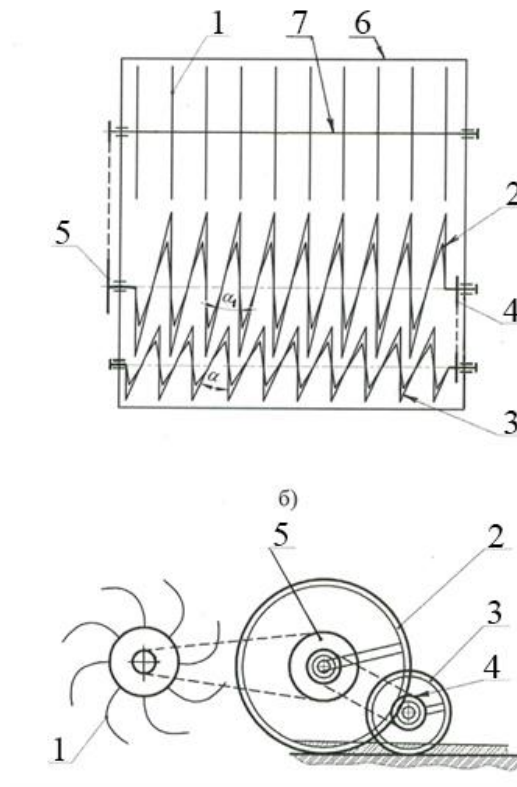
Схема ротаційного ґрунтообробного знаряддя (а – вигляд зверху; б – у робочому положенні): 1 – диски голчасті; 2, 3 – спіральньо-гвинтові робочі органи; 4 – синхронізувальна ланцюгова передача; 5 – ланцюгова передача приводу; 6 – рама знаряддя; 7 – вал [5].
